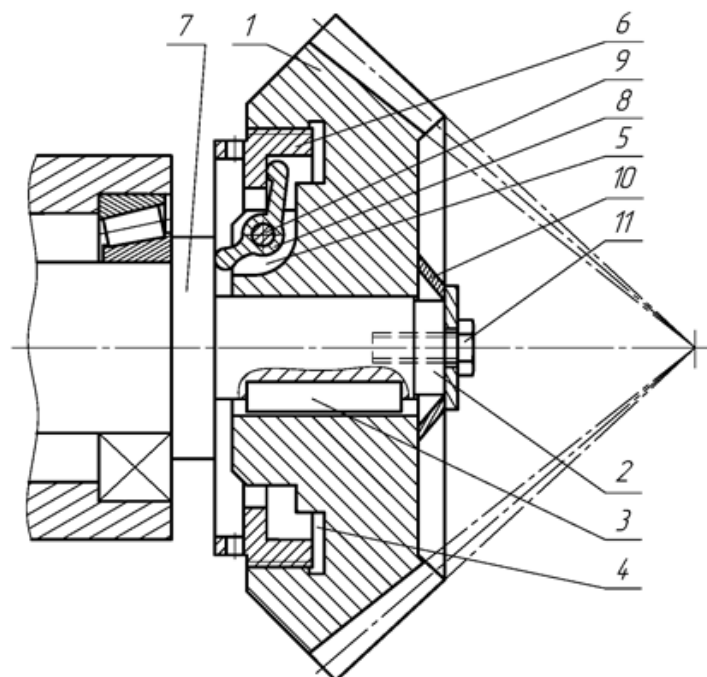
Пристрій для регулювання зачеплення конічних шестерень
